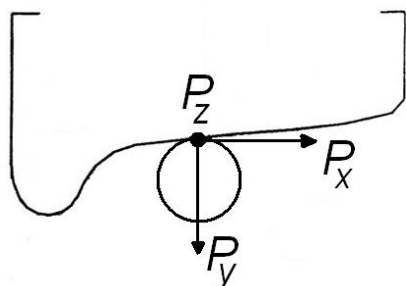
Расчетная схема для определения упругих перемещений сборного чашечного резца
